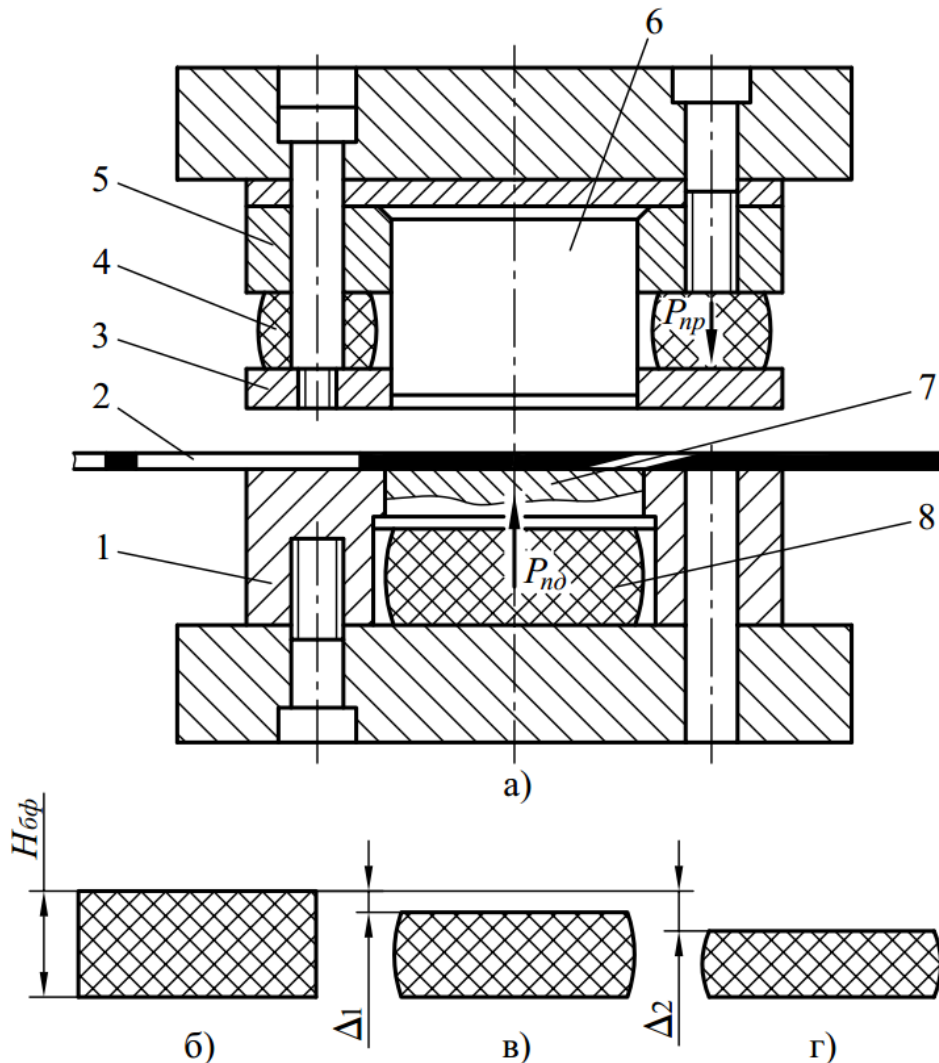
Штамп з верхнім і нижнім притискуванням для вирубівання заготовки:
